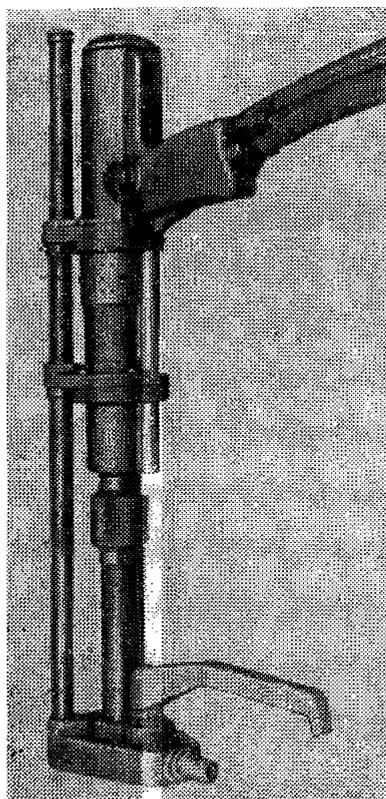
Общий вид пневматической сверлильной машины типа ИП-1023
